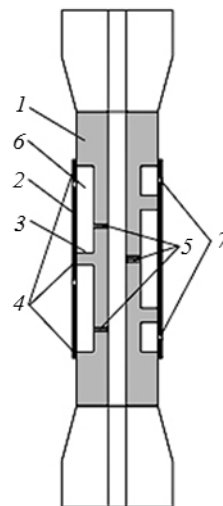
Чертеж двустенного образца, изготовленного диффузионной сваркой:
